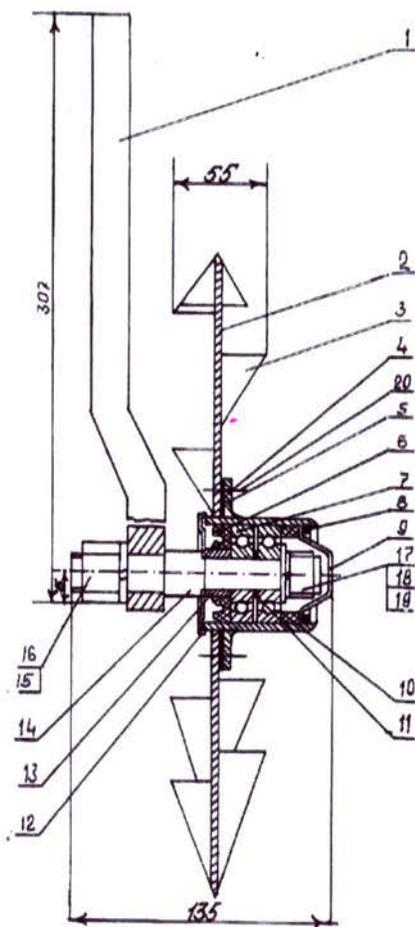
Рабочий орган для междурядной обработки хлопчатника - разрушения почвенной корки и уничтожения сорной растительности. 1-стойка; 2-рабочий диск; 3-режущие пластины; 4-прокладка; 5-корпус подшипника; 6-сальник; 7-подшипник; 8-стопорное кольцо; 9-крышка; 10-уплотнитель; 11-упорная промежуточная шайба; 12-пыльник; 13-упорная втулка; 14-ось; 15-гайка; 16-шайба; 17-гайка; 18-шайба; 19-шайба; 20-винт.
